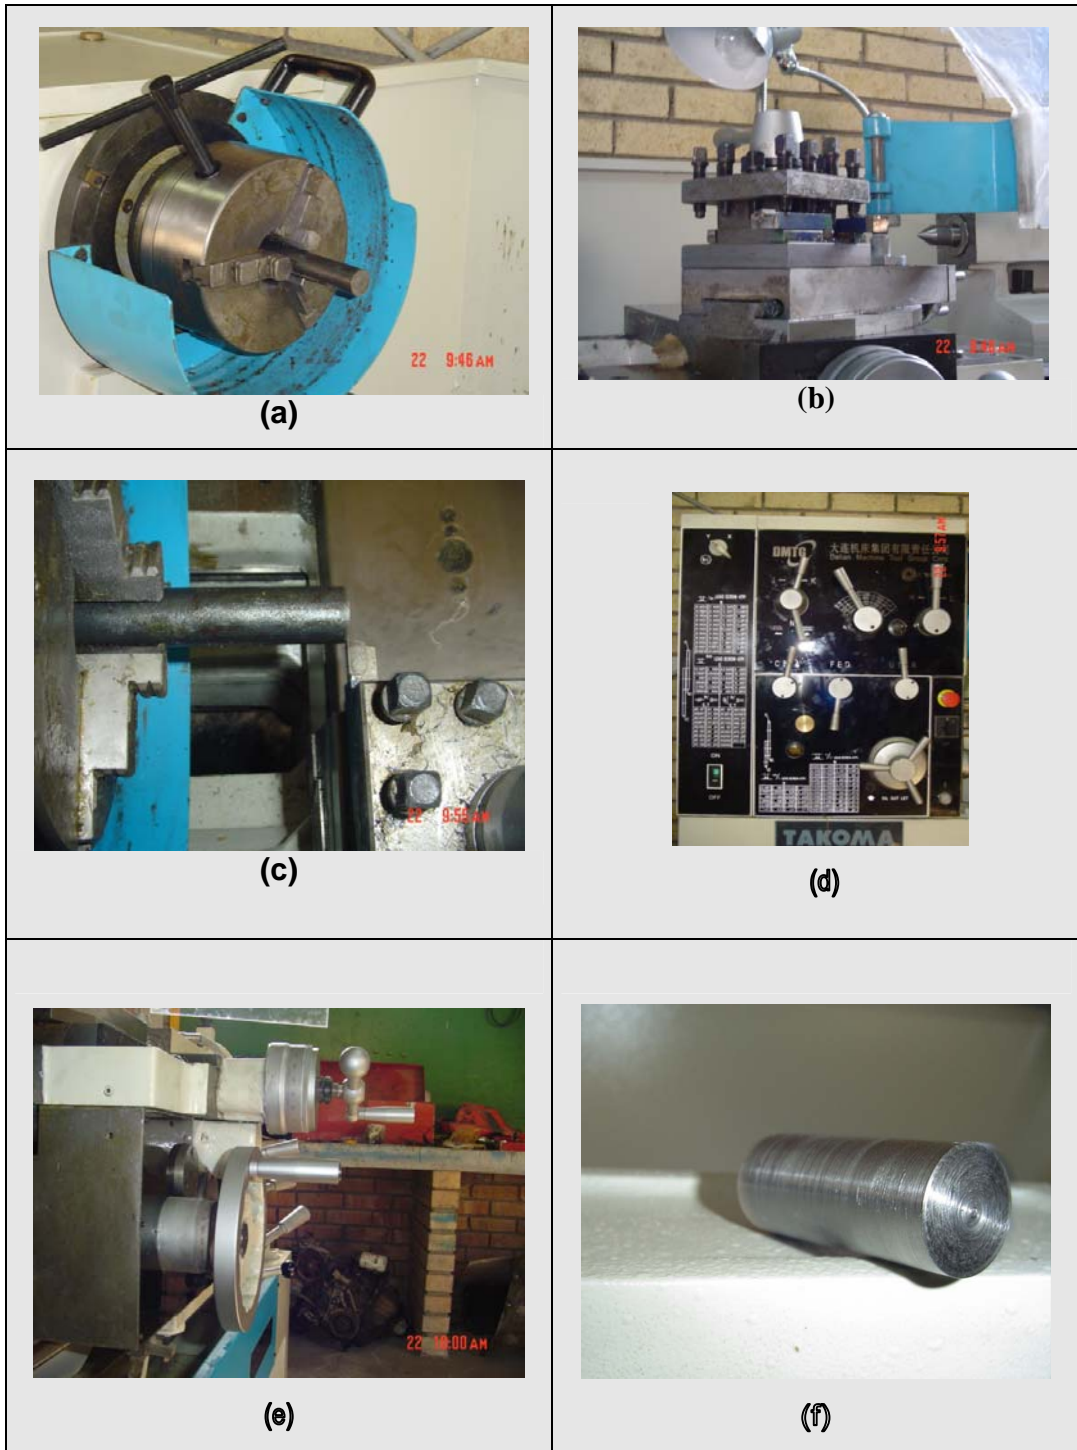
Cilindrar. (a) colocación de la pieza en la copa de trabajo, (b) colocación de la herramienta en el portaherramientas, (c) aseguramiento de la altura de corte, (d) selección de la velocidad del husillo, (e) desplazamiento longitudinal de la herramienta de corte, (f) pieza terminada.
